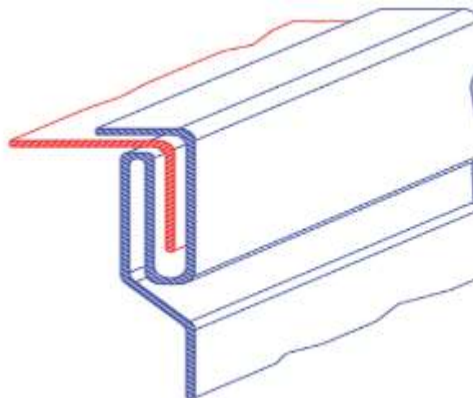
Sistema de Cravamento Longitudinal Pittsburg
